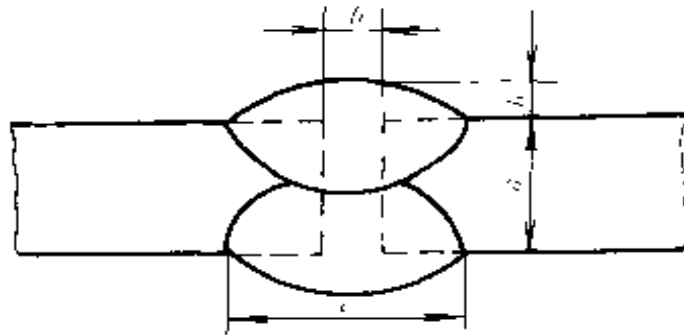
J形坡口双面对接 TIG 焊的焊缝截面
